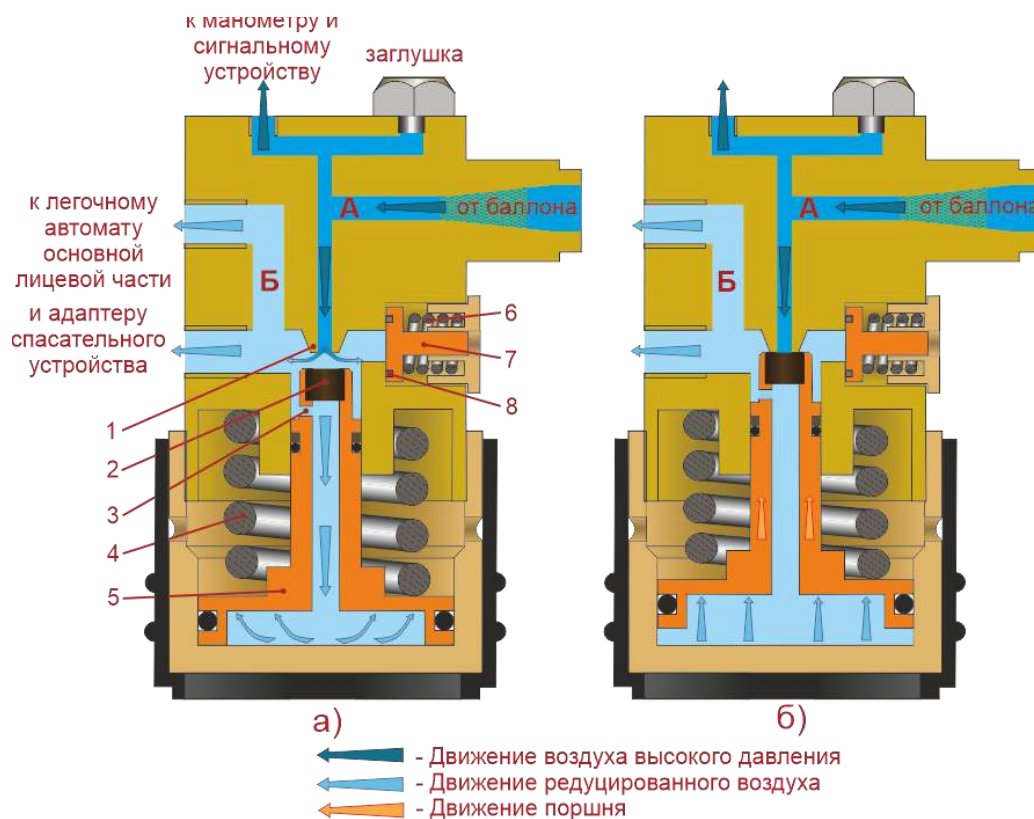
Устройство редуктора ПТС 11.02.00.000
